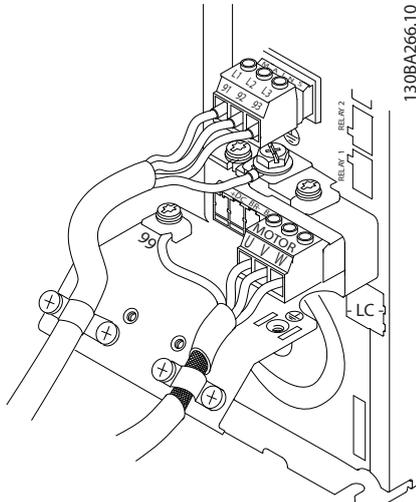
Befestigung der Zugentlastungsklemme
